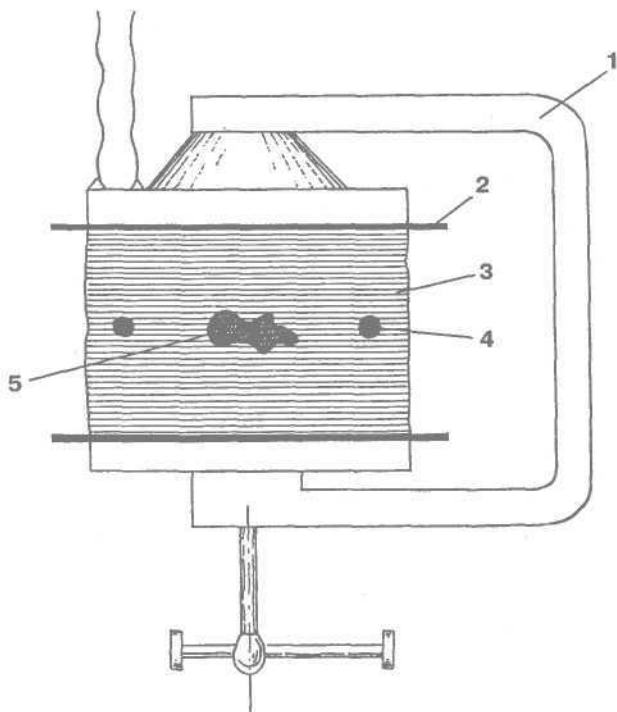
Изготовление резиновой пресс-формы: 1 — вулканизатор; 2 — стальные пластины; 3 — сырая резина; 4 — замок (стальные шарики); 5 — образец
